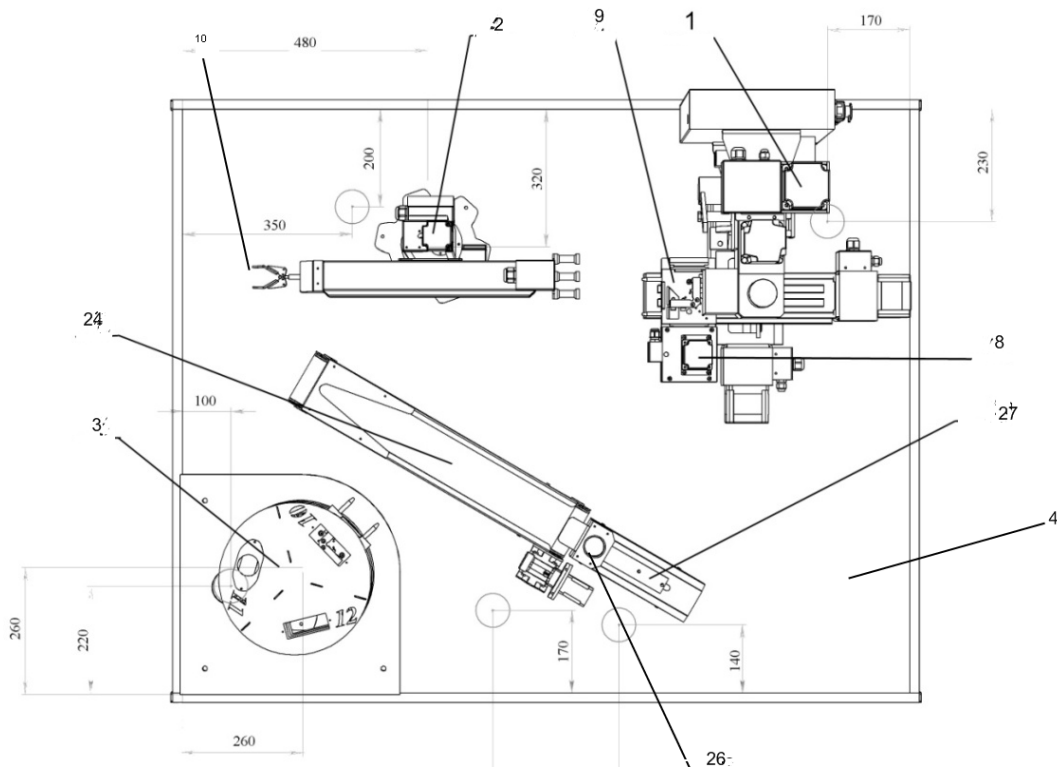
Учебная ГПМ на базе учебного фрезерного станка с компьютерной системой ЧПУ: 1 – фрезерный станок; 2 – робот; 3 – многоярусный накопитель приспособлений спутников с заготовками; 4 – подиум; 8 – устройство зажима приспособления-спутника; 9 – приспособление-спутник; 10 – схват робота; 24 – транспортер; 26 – питатель; 27 – толкатель
